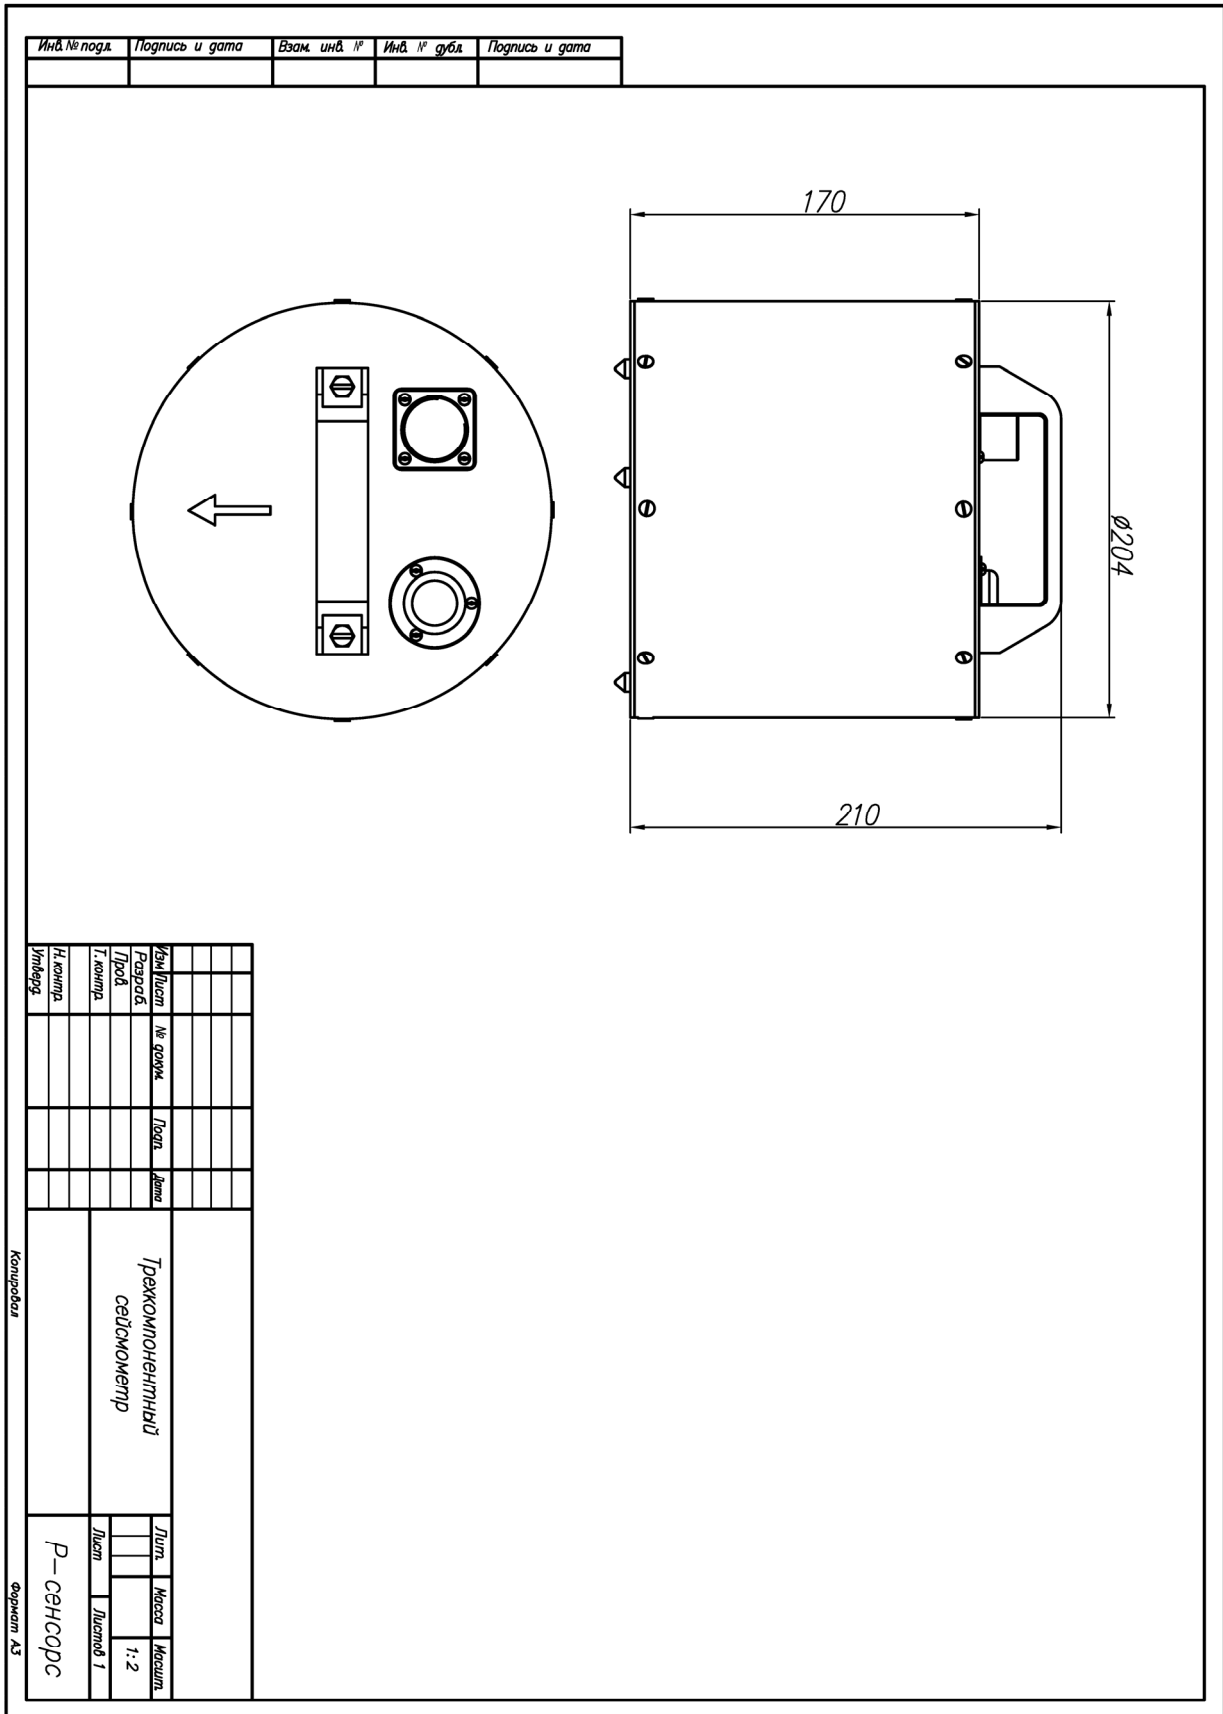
Габаритный чертёж сейсмометра СМЕ-6111.
